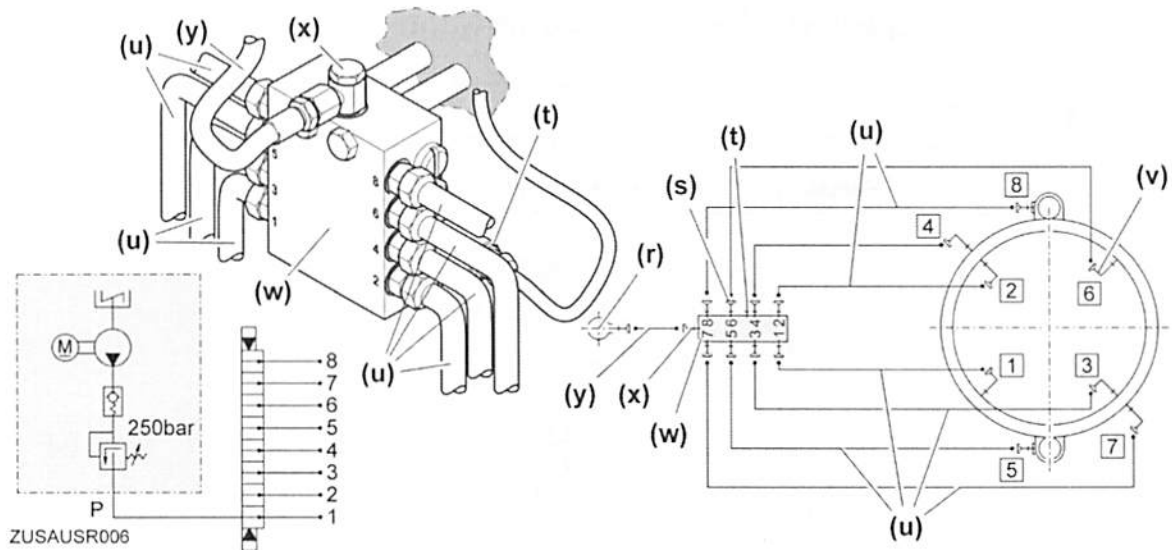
Verlegeplan und Hydraulik-Schaltplan (8er-Verteiler mit zwei Drehwerken)
